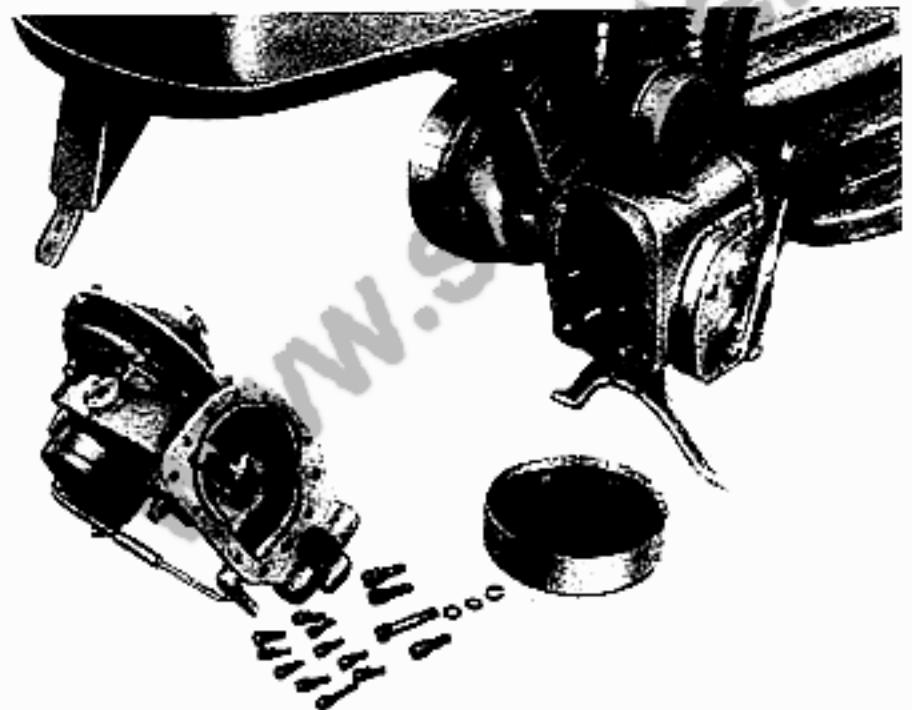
Smontaggio corpi e ingranaggi cambio
